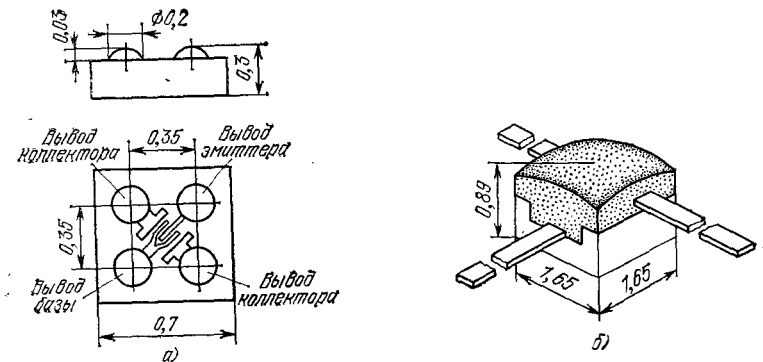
Конструкция бескорпусного биполярного транзистора с шариковыми (а) и балочными (б) выводами
